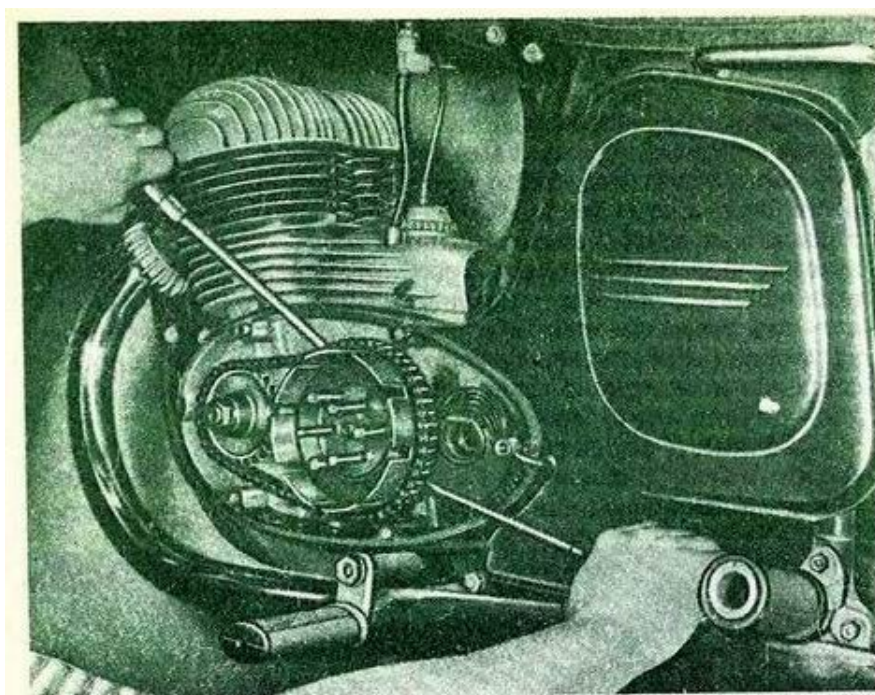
Отжатие двумя отвертками барабана для сдвига опорного диска
